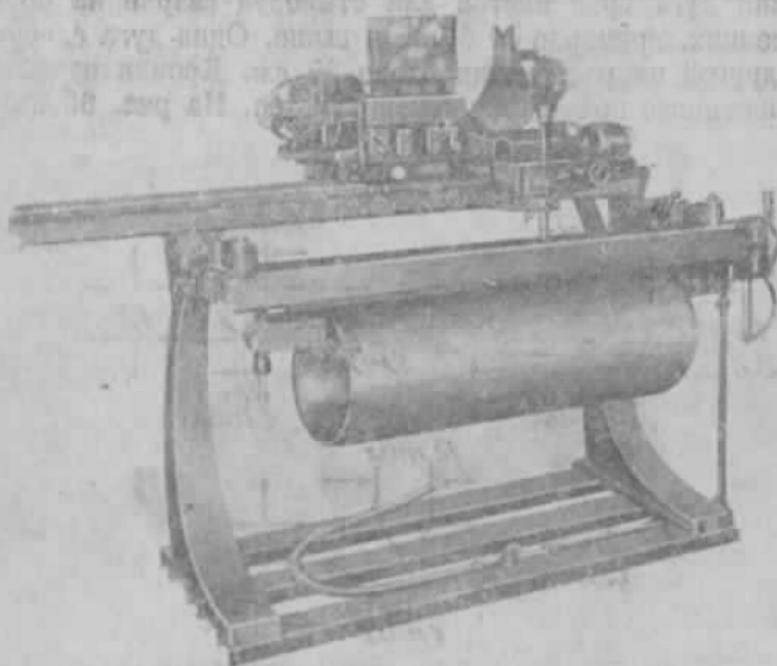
Зажимное приспособление для автоматической сварки.
